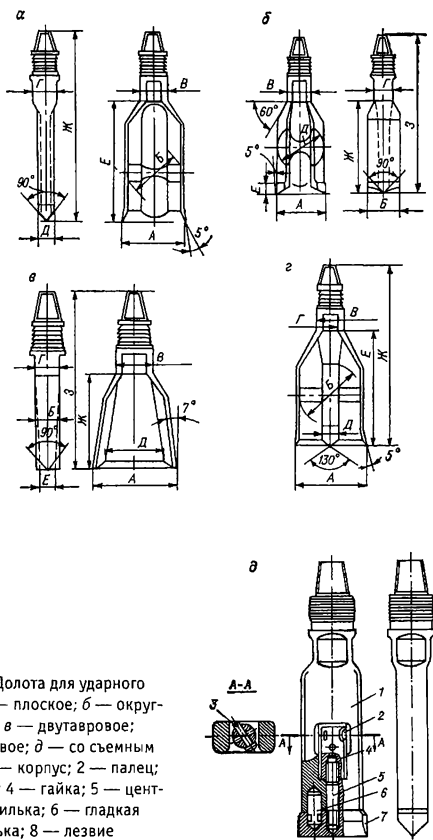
Долота для ударного бурения: а — плоское; б — округляющее; в — двутавровое; г — крестовое; д — со съемным лезвием: 1 — корпус; 2 — палец; 3 — шплинт; 4 — гайка; 5 — центровая шпилька; 6 — гладкая шпилька; 8 — лезвие
